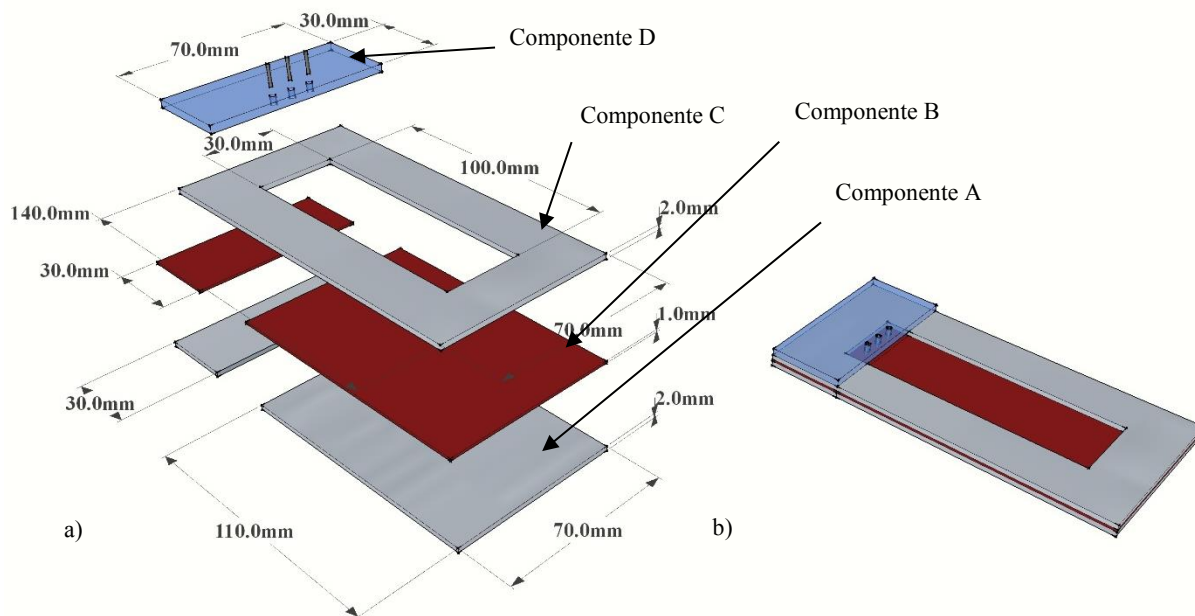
a) Sistema de restrição de pastas de cimento; b) sistema assembledo.
